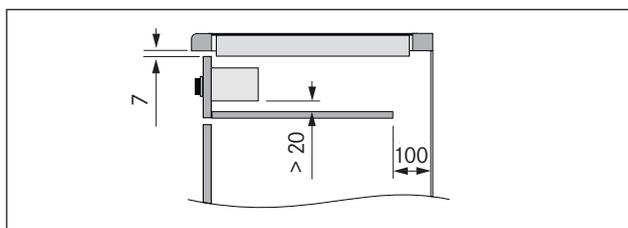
Vista laterale piano di protezione cavi e aerazione
